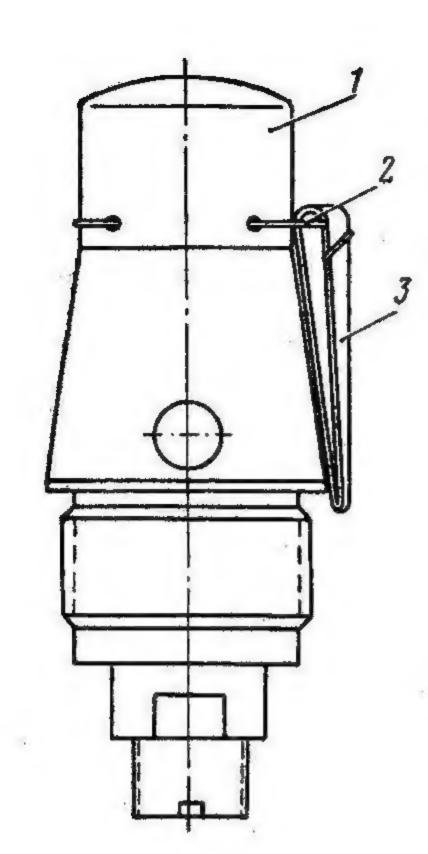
Взрыватель ГПВ-2 (общий вид): 1 — колпачок; 2 — чека; 3 — тесьма
